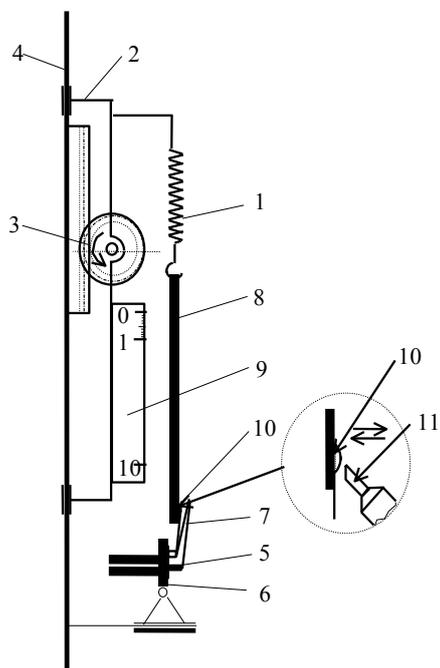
Кинематическая схема прибора для определения прочности сварок.
